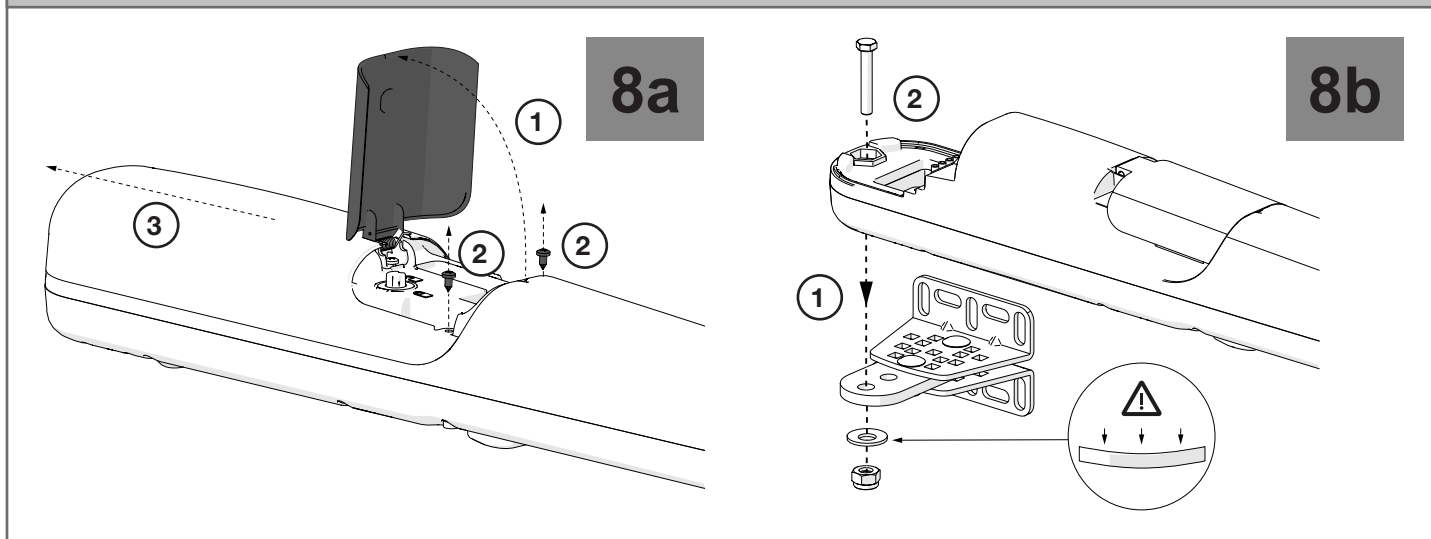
FR - Fixation du motoréducteur et du chevron avant
